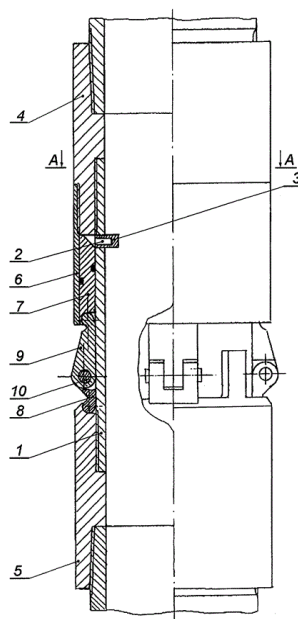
Центратор гидравлический: 1 – корпус; 2 – сквозные радиальные каналы; 3 – разрушаемые пробки; 4, 5 – муфты; 6 – рабочий цилиндр; 7 – поршень; 8, 9 – основные и дополнительные центрирующие элементы; 10 – шарнирные соединения
